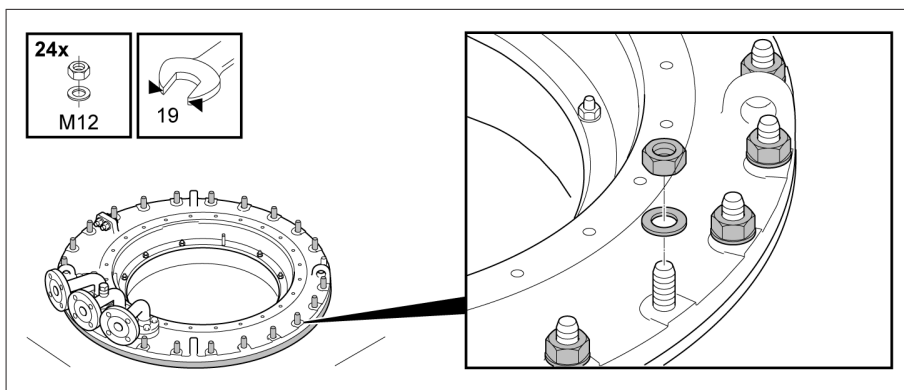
Parafusar o cabeçote do comutador de derivação em carga com o flange de montagem.
